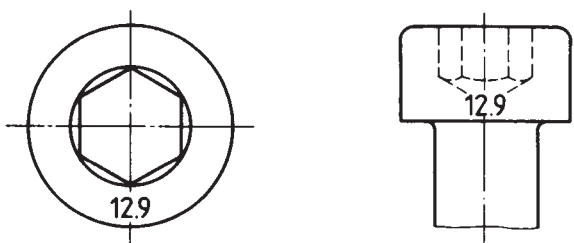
Beispiele für die Kennzeichnung von Zylinderschrauben mit Innensechskant
